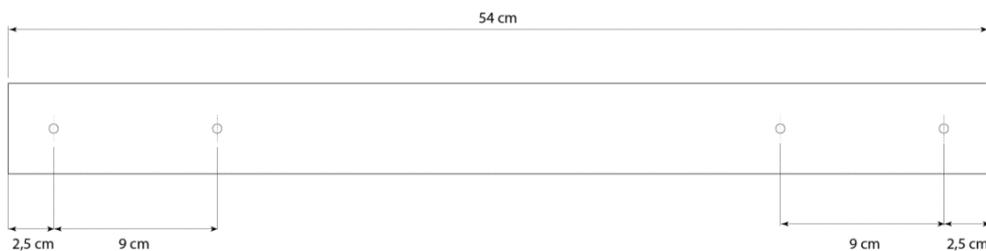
Desenho técnico da lâmina que constitui o módulo I.
